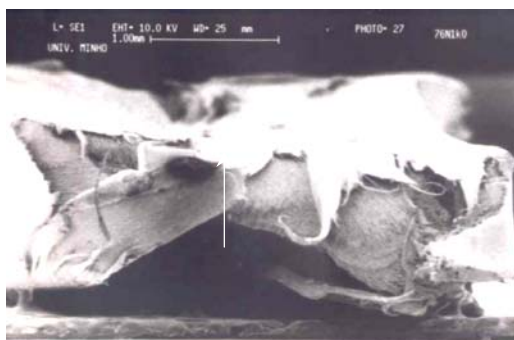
Imagens SEM de superfícies de fractura - PEAD 7731
